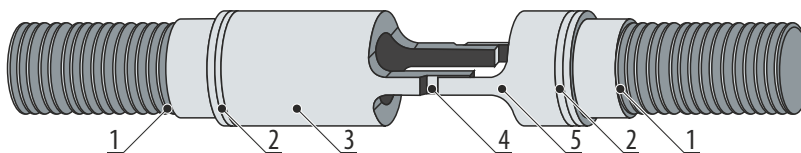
Эскиз образца для испытаний сварного соединения трубы направляющего канала и наконечника: 1 — концевая деталь; 2 — сварной шов; 3 — труба направляющего канала; 4 — исследуемый сварной шов; 5 — втулка наконечника направляющего канала
